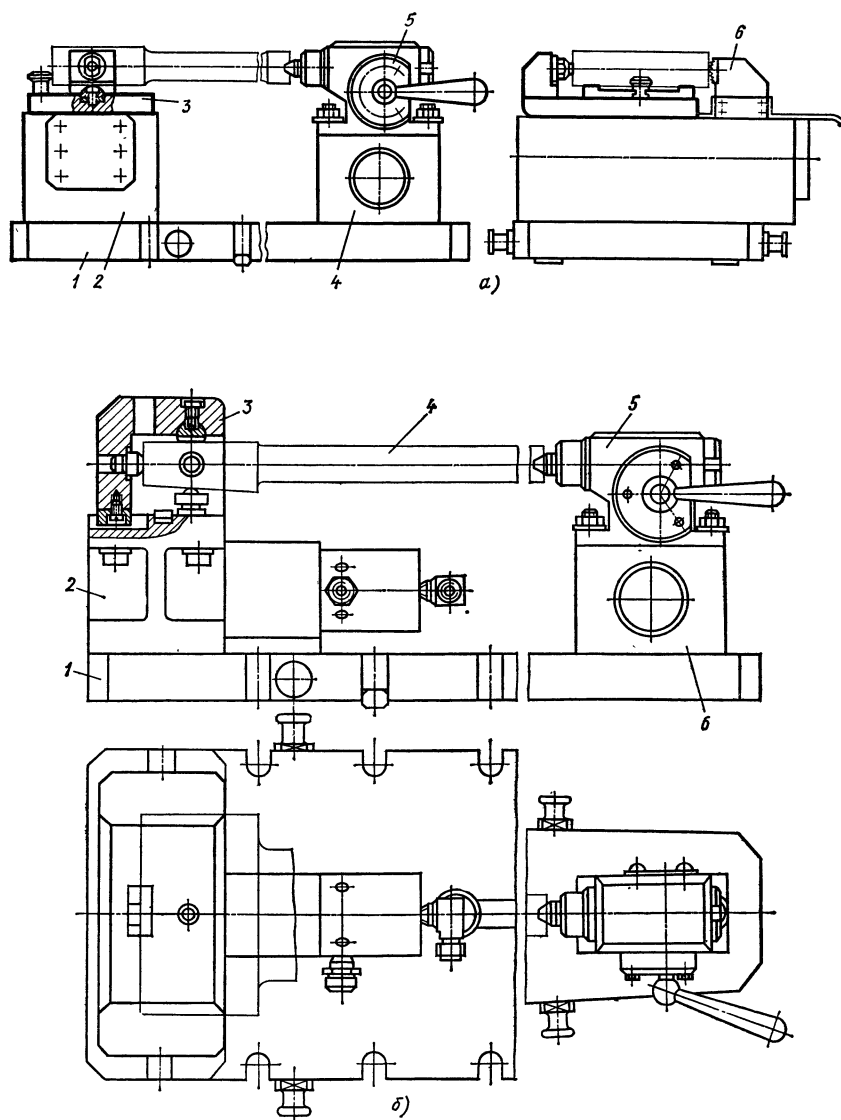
Специализированные наладочные приспособления для фрезерования галтели:
